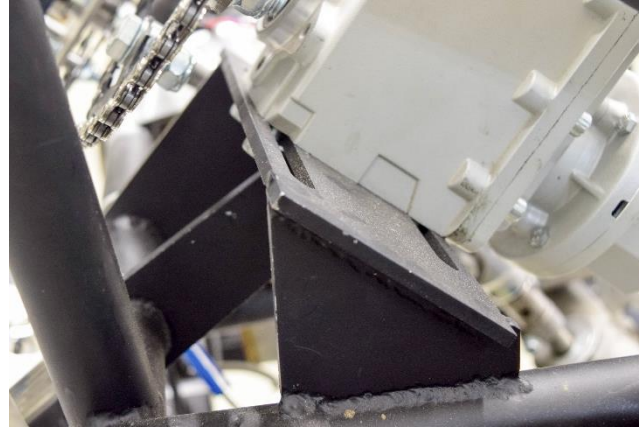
Soporte construido y soldado al bastidor del prototipo
